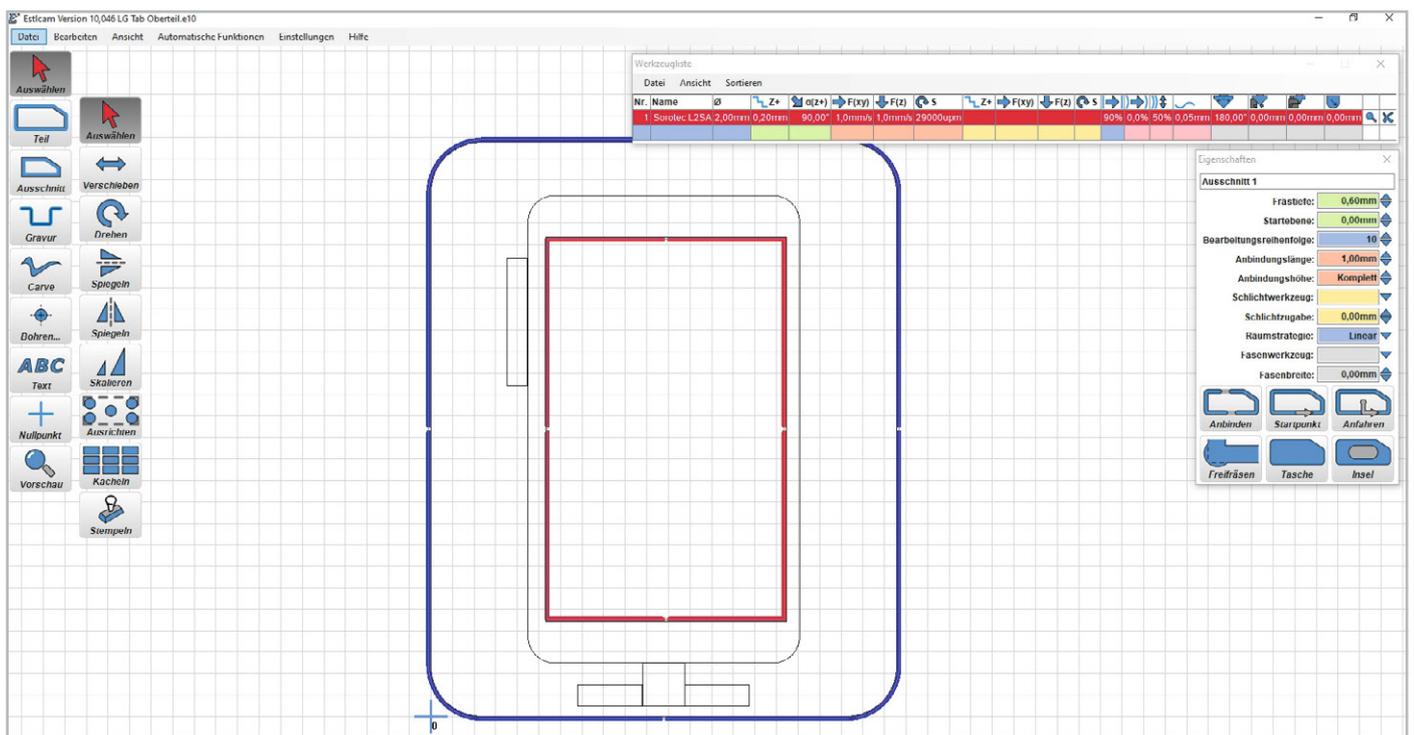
Fräseinstellungen für das Gehäuseoberteil
